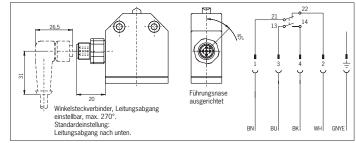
Maßzeichnung/Anschlussplan SN01.558SVM5 mit Steckverbinder M12 (SVM5, 5-polig)
